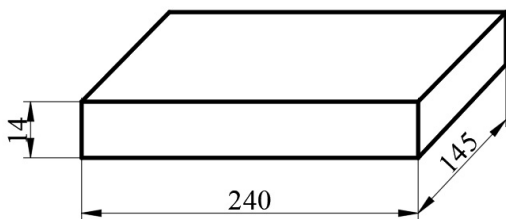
Эскизный чертеж заготовки в виде пластины с размерами: 14 × 145 × 240 мм
